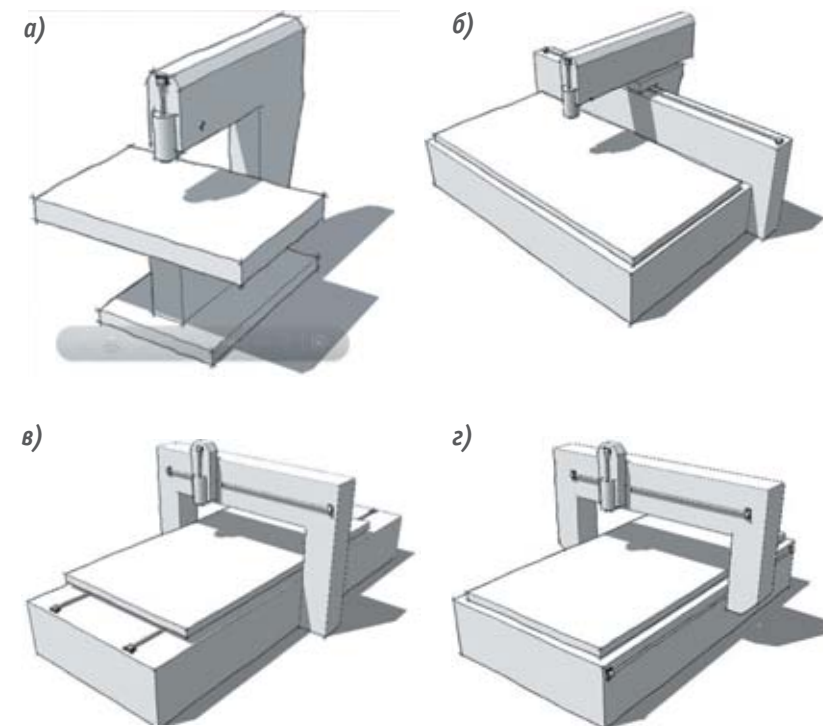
Наиболее распространенные схемы конструкции фрезерных станков с ЧПУ:
